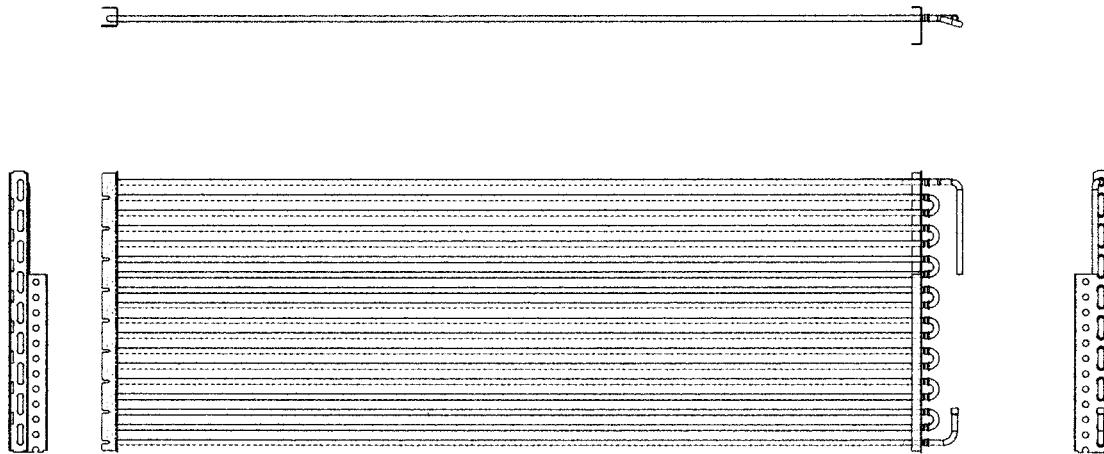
Circuito para intercambiador de calor hecho de una sola pieza.
